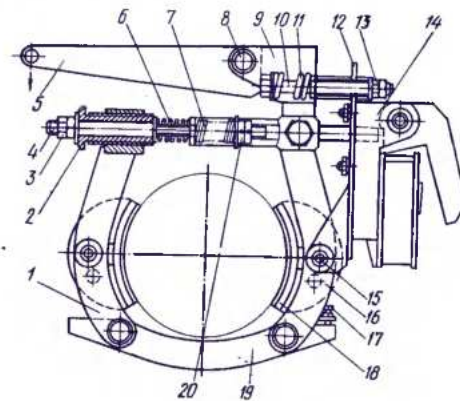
Тормоз механизма поворота крана КС-4561А:
